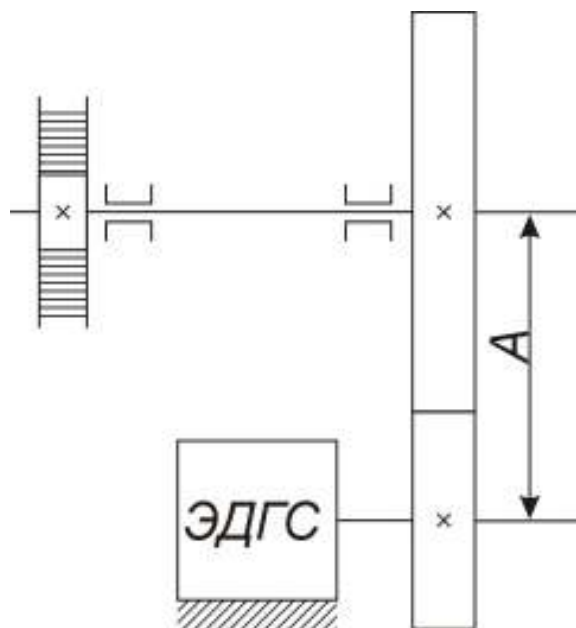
2 Схема одноступенчатой цилиндрической зубчатой передачи
